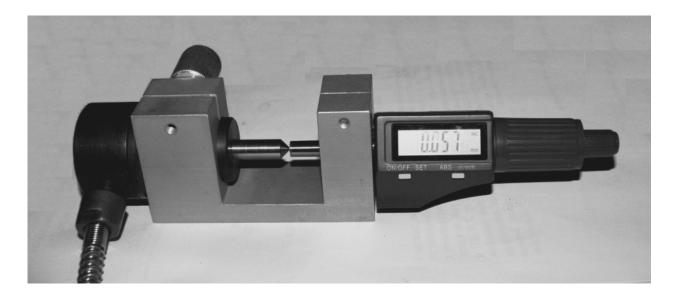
Калибровочное приспособление датчика паперечного расширения ДПР-05.
